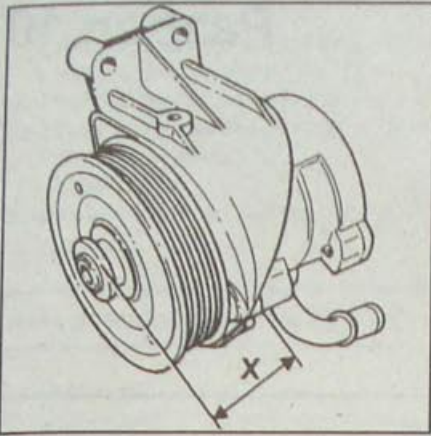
Место измерения размера (X=66,8 мм) при запрессовке втулки шкива насоса усилителя рулевого управления на автомобилях с двигателями G8T
